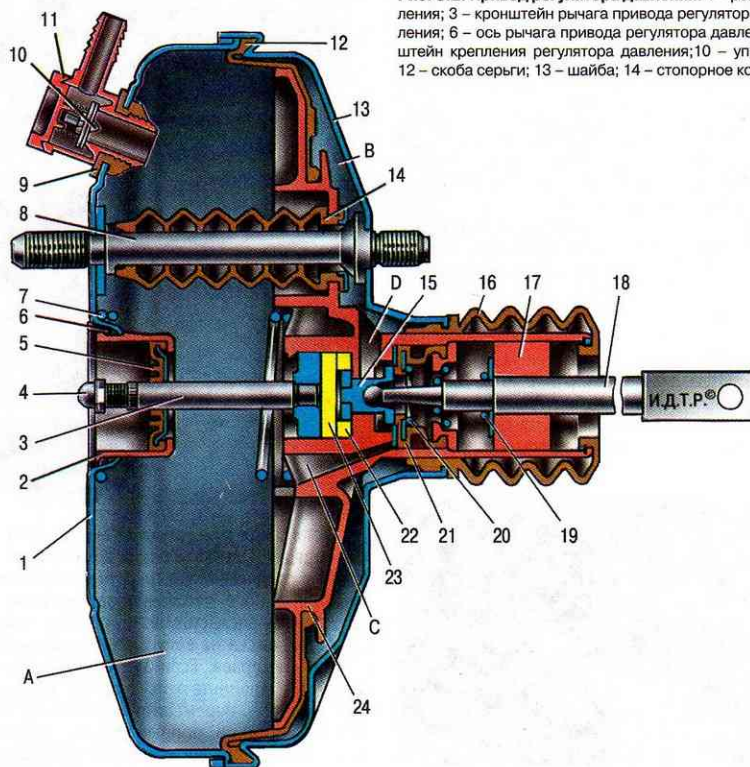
Вакуумный усилитель: 1 – корпус вакуумного усилителя; 2 – чашка корпуса усилителя; 3 – шток; 4 – регулировочный болт; 5 – уплотнитель штока; 6 – уплотнительное кольцо фланца главного цилиндра; 7 – возвратная пружина диафрагмы; 8 – шпилька усилителя; 9 – фланец крепления наконечника; 10 – клапан; 11 – наконечник шланга; 12 – диафрагма; 13 – крышка корпуса усилителя; 14 – уплотнительный чехол; 15 – поршень; 16 – защитный чехол корпуса клапана; 17 – воздушный фильтр; 18 – толкатель; 19 – возвратная пружина толкателя; 20 – пружина клапана; 21 – клапан; 22 – втулка корпуса клапана; 23 – буфер штока; 24 – корпус клапана; А – вакуумная камера; В – атмосферная камера; С, D – каналы
